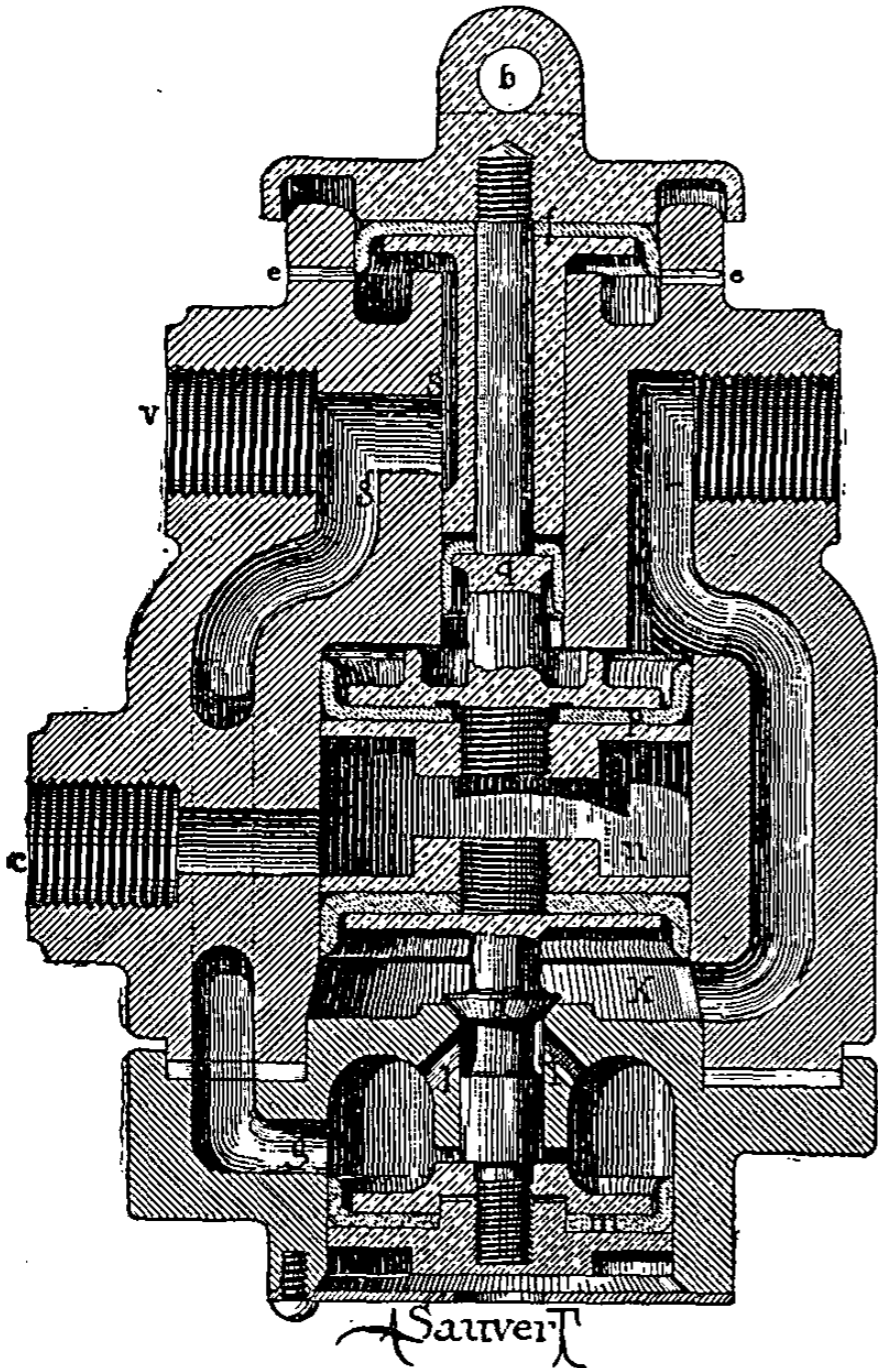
Frein à air comprimé. Distributeur Soulerin. Coupe.
